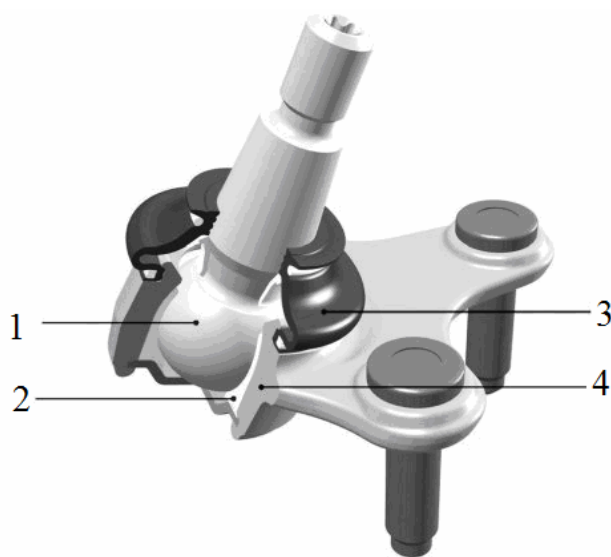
Шаровая опора (1- шаровая цапфа; 2 – вкладыш; 3 – пыльник; 4 – корпус)
